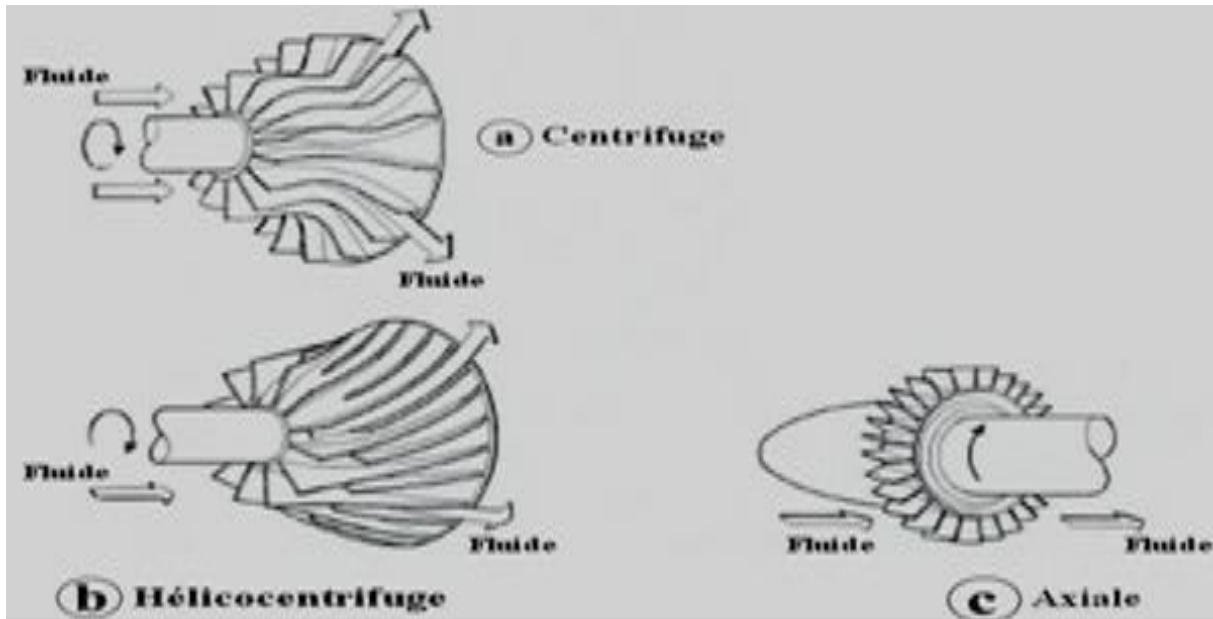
Roues mobiles de machines centrifuge, hélico centrifuge et axiale. [6]
